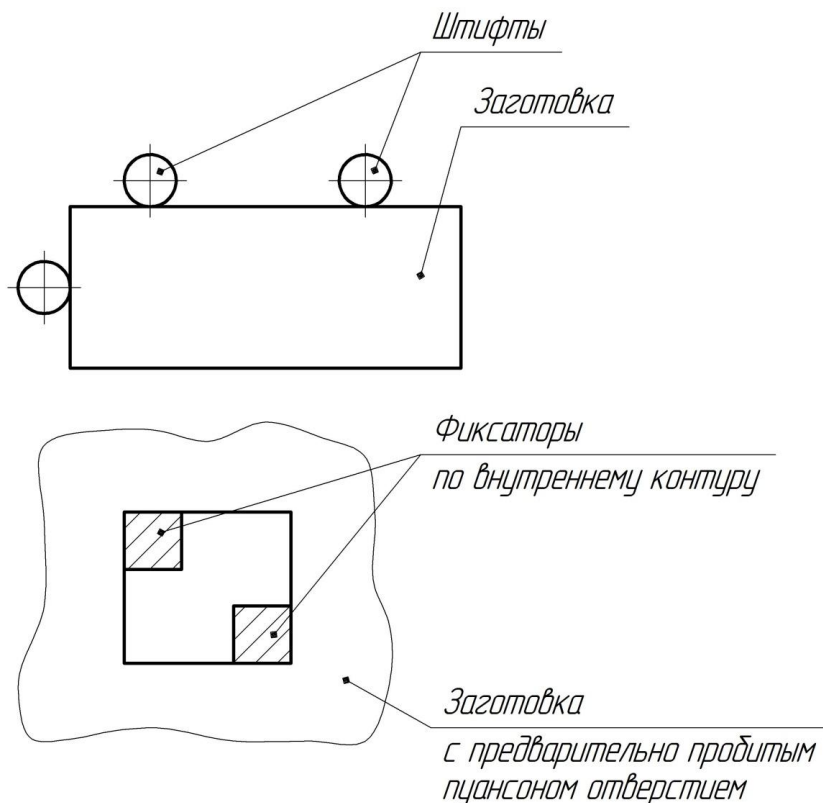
Фиксаторы заготовок перед штамповкой
